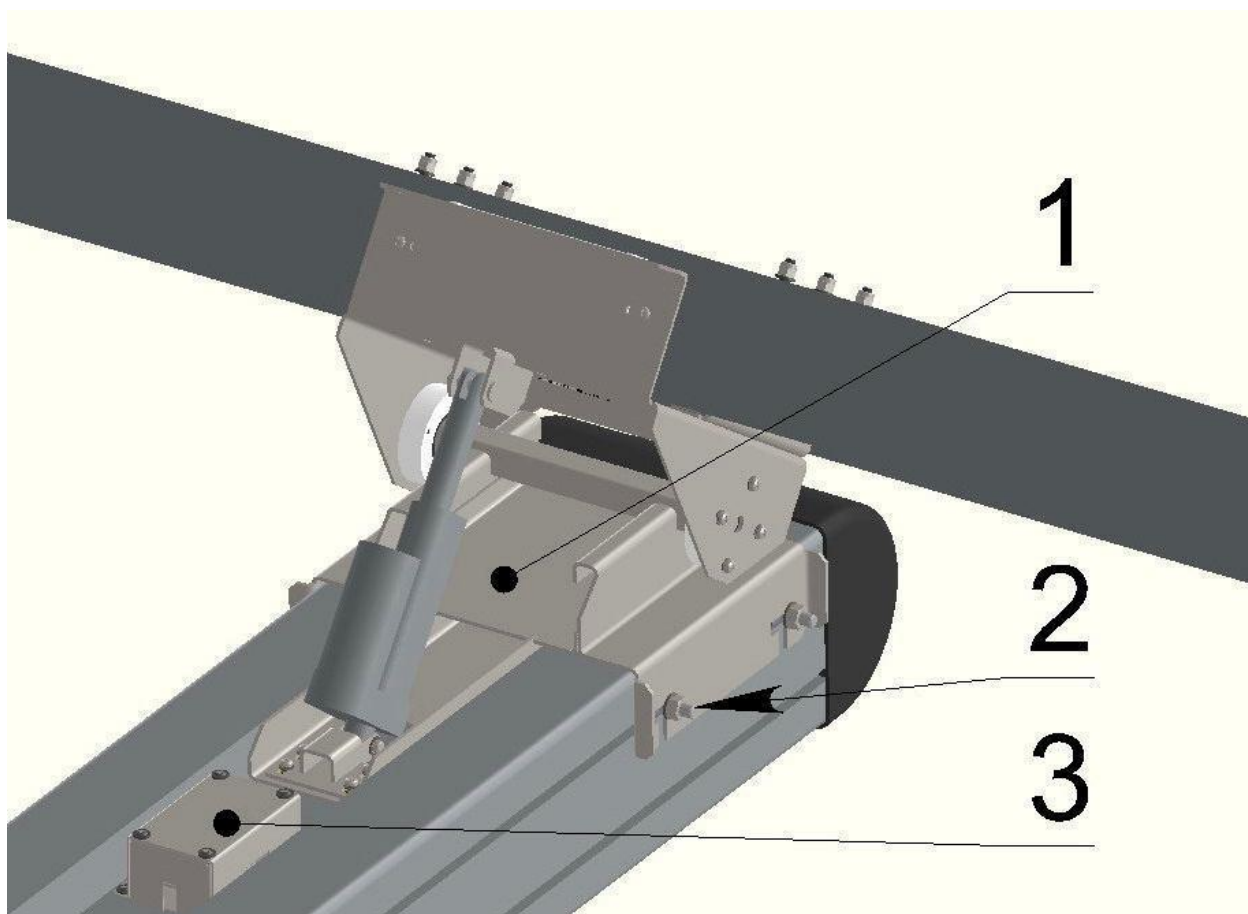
Установка привода наклона на балку. 1- привод наклона с балкой; 2-пластиковая вставка с болтом М8х20, гайкой М8 и шайбой; 3- корпус платы управления привода наклона.
